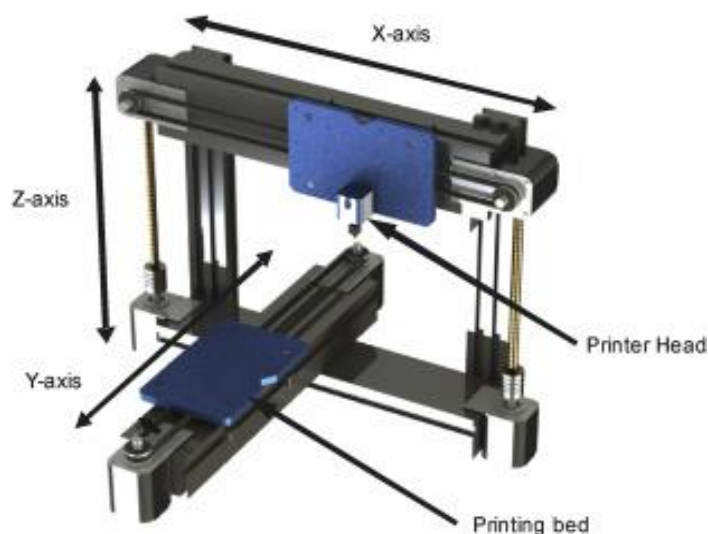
Απεικόνιση τρισδιάστατης κίνησης κεφαλής σε 3d Printer [21]
